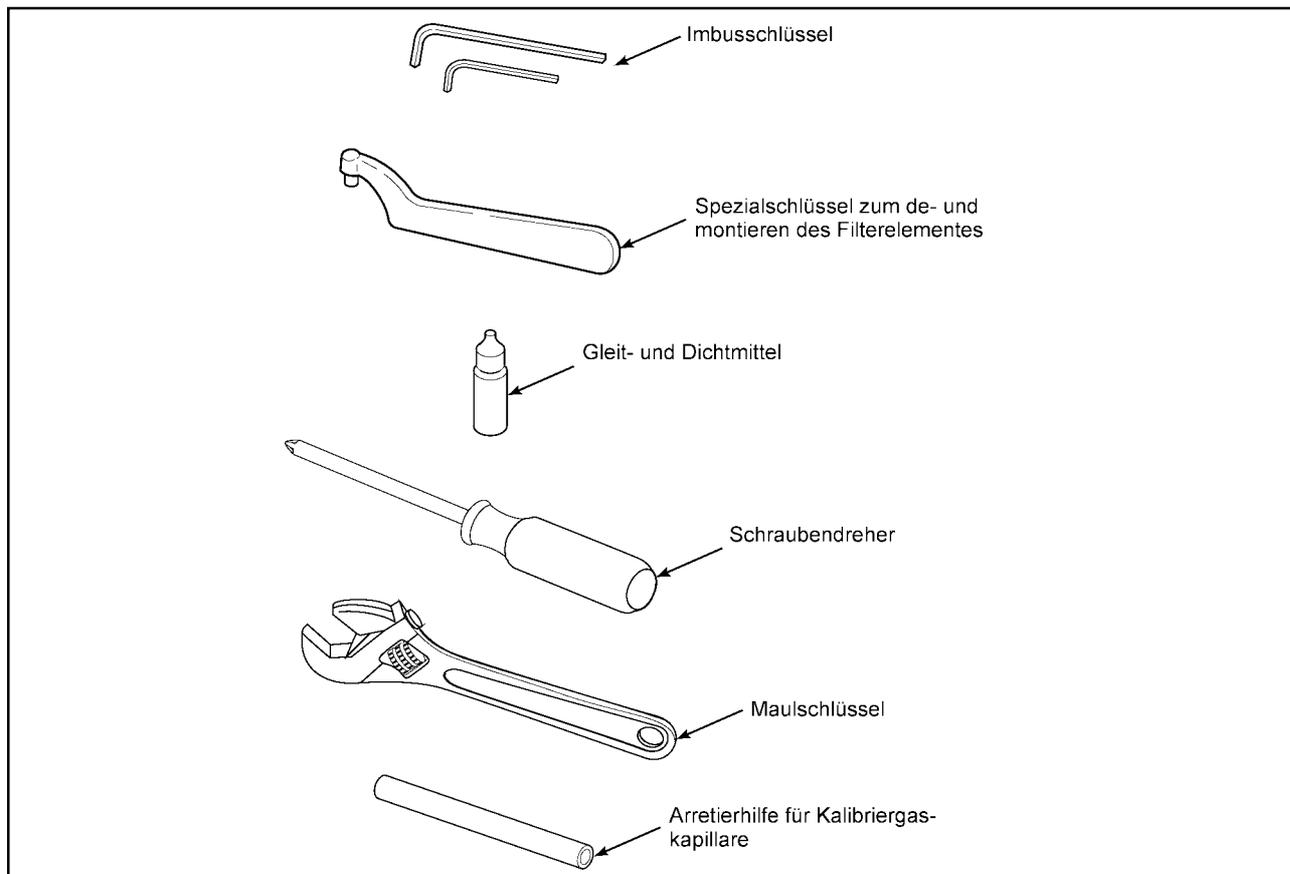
Werkzeugsatz zur De- und Montage des Oxymitter 4000
